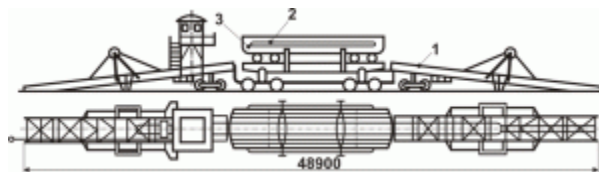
Передвижной боковой платформоопрокидыватель
